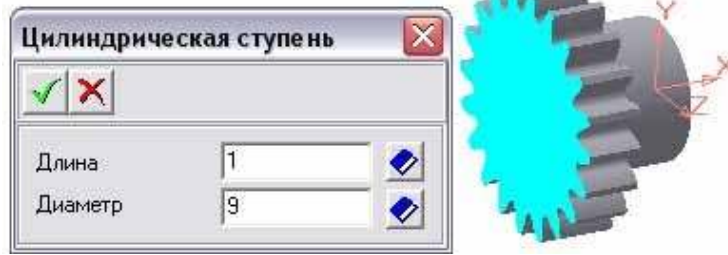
Додавання на торцевій площині диска зубчастого колеса циліндричного виступу
